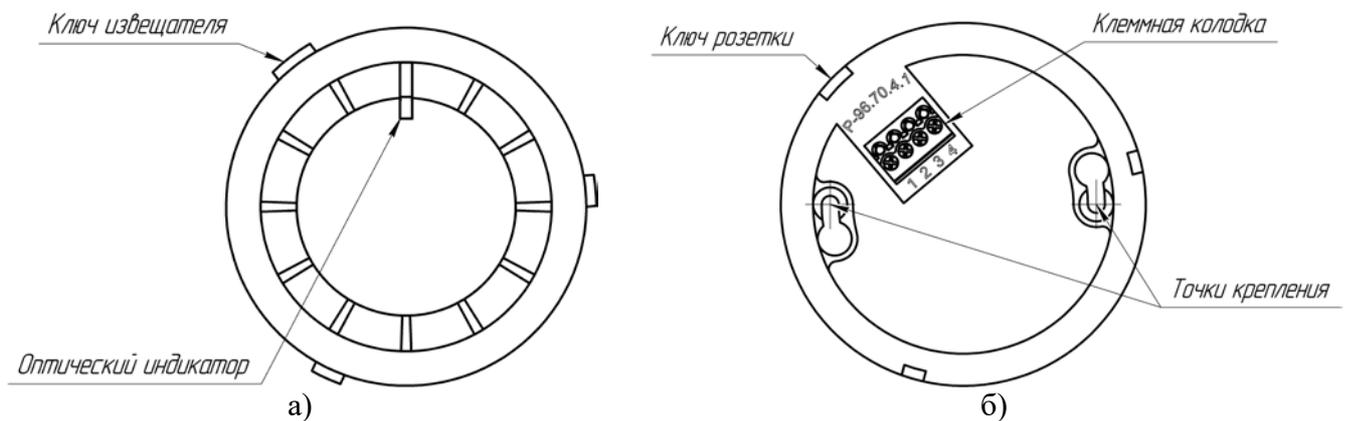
Конструкция извещателя, (а) - извещатель, (б) - розетка.
